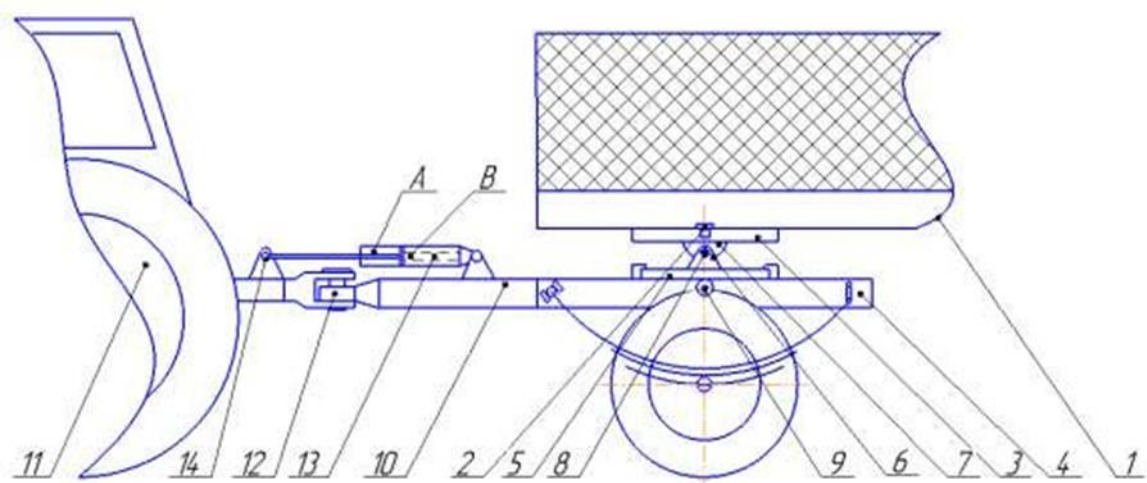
Тягово-зчіпний пристрій причепа з поперечно-переміщуваною поворотною платформою – вигляд збоку
